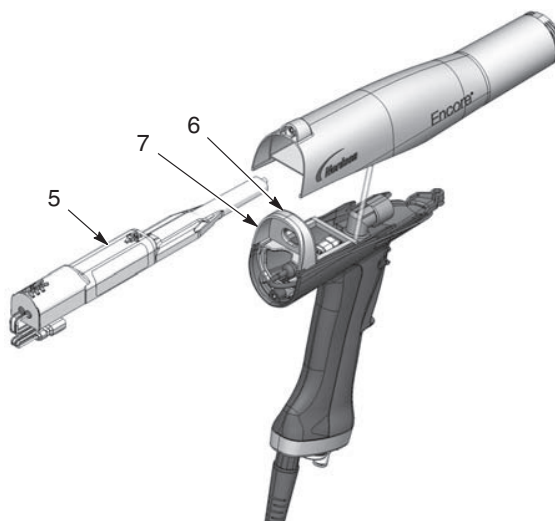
Demontáž tělesa pistole z rukojeti
